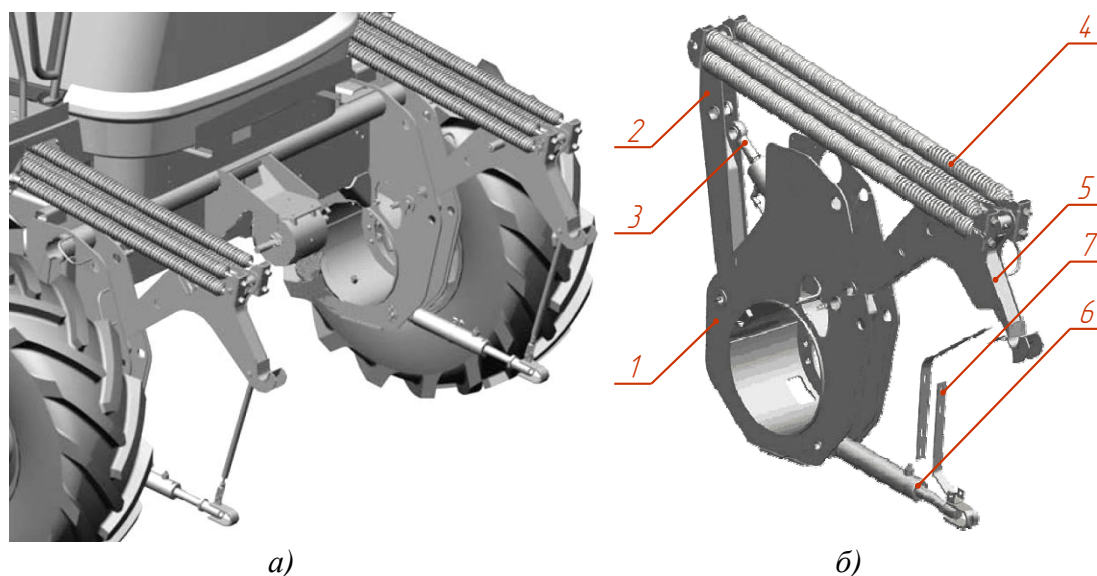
Механизм агрегатирования на раме косилки (а) и на общем виде (б): 1 – рама; 2, 5 – двуплечий поворотный рычаг; 3 – гидроцилиндр подъема; 4 – блок уравнивающих пружин с телескопической тягой; 6 – гидроцилиндр угла атаки; 7 – растяжка (из открытых источников)
